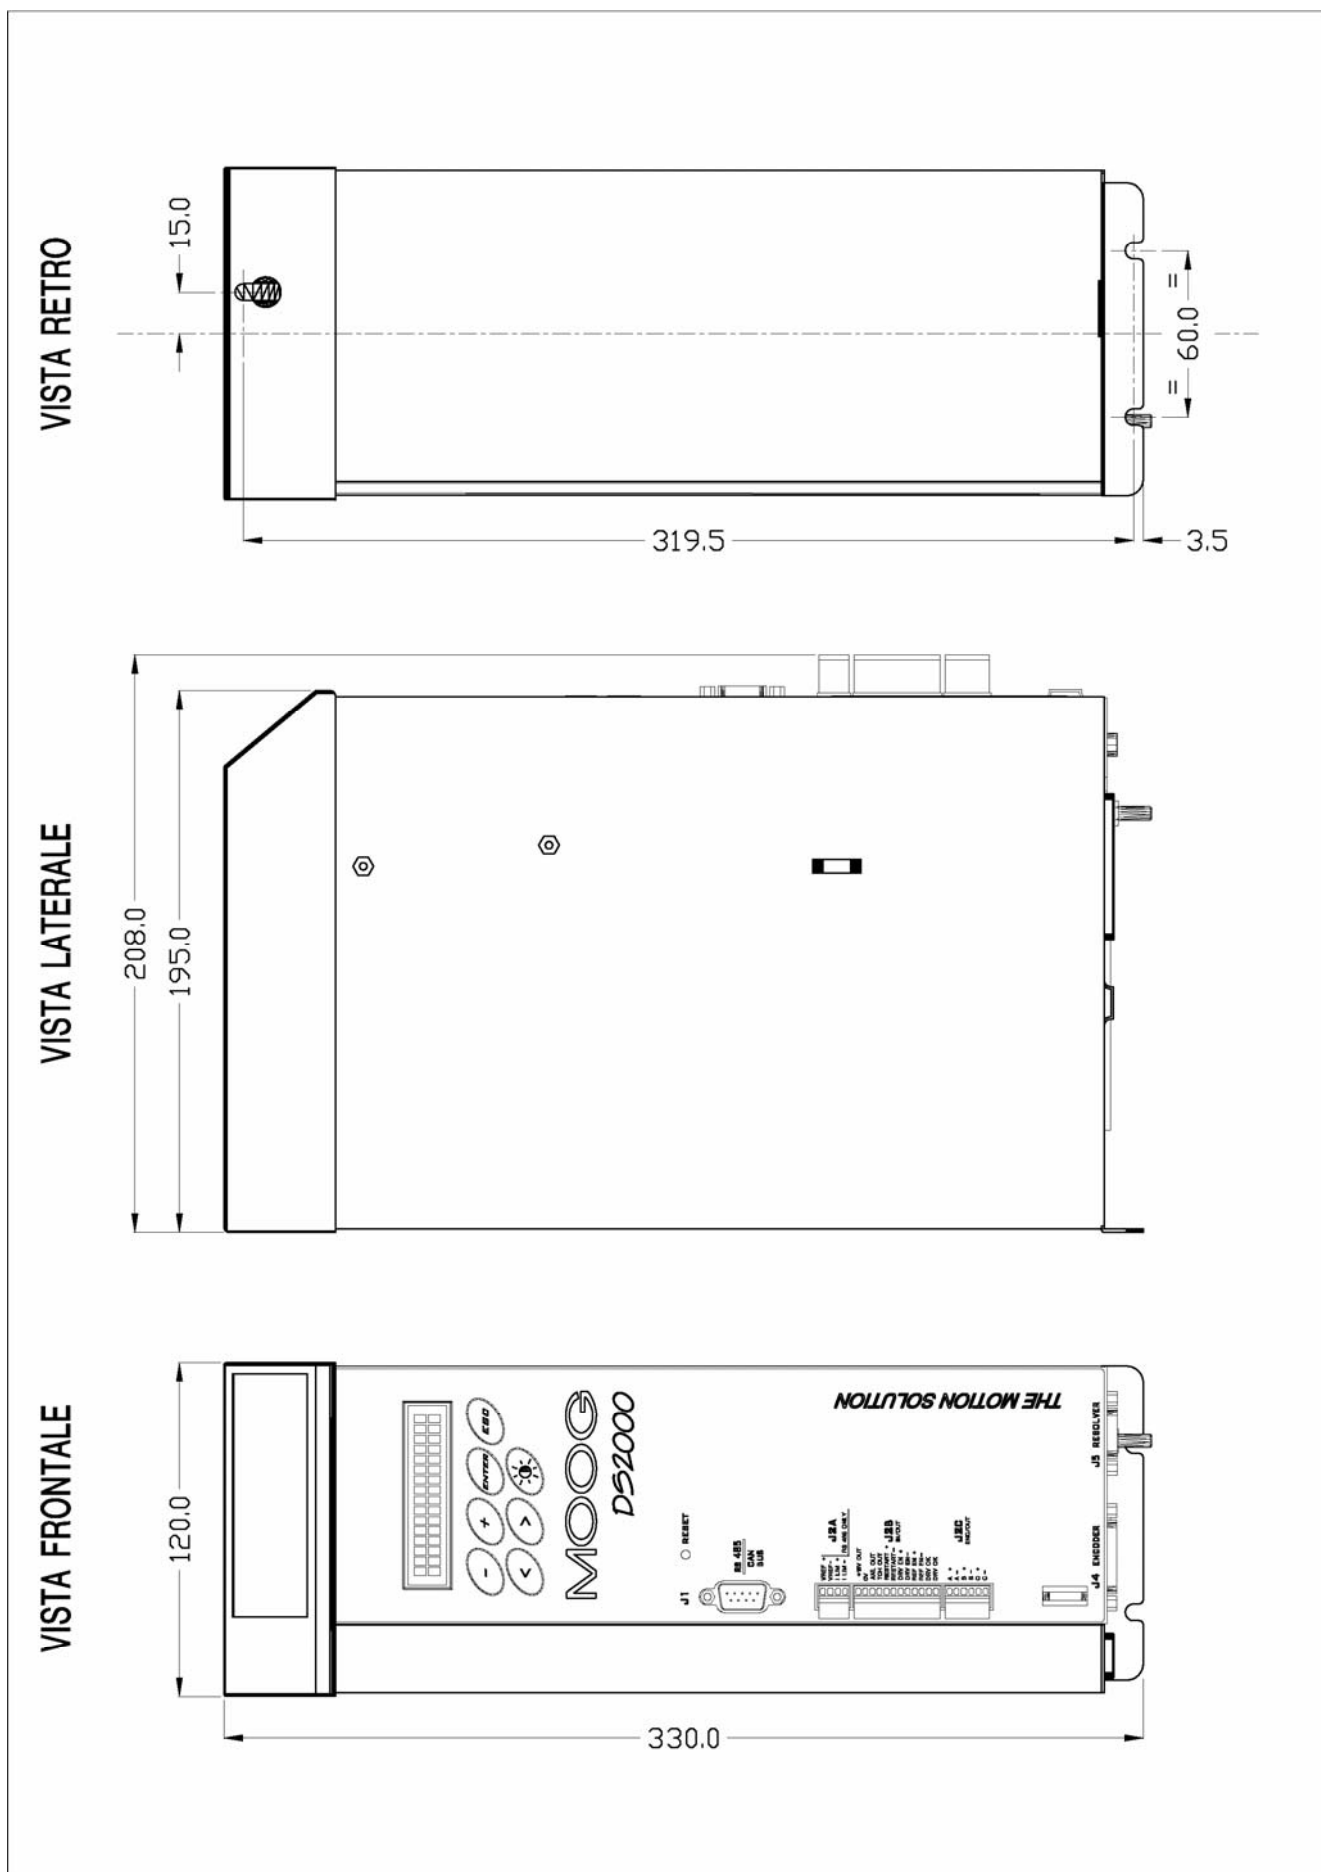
Dimensioni e fissaggi (mm) taglia B
